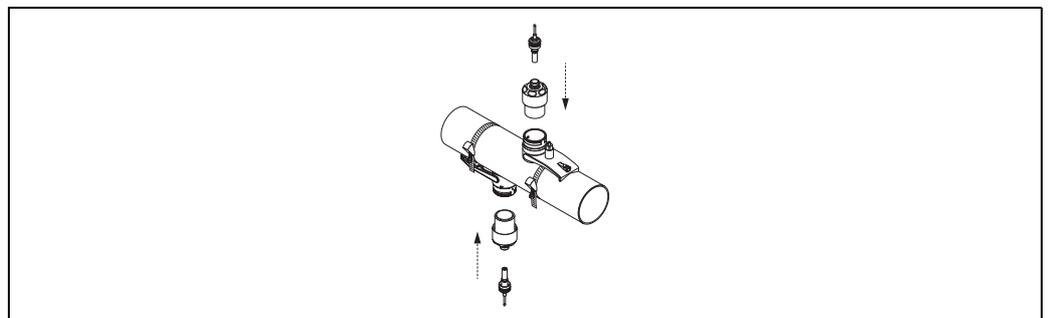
Montaggio del sensore e collegamento del cavo di collegamento
